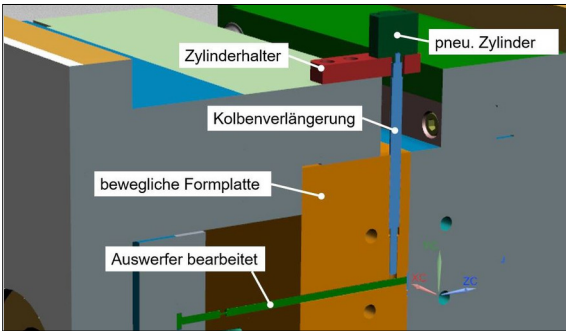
Schnitt durch Werkzeug mit Versuchsaufbau
